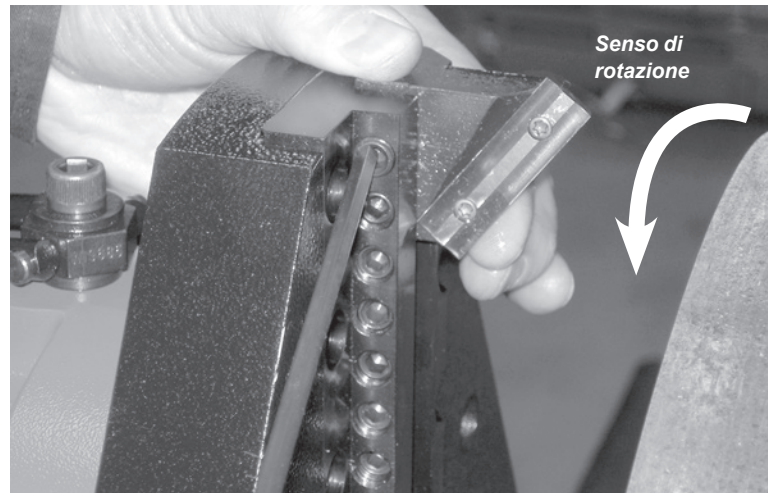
Inserire l'utensile nel portautensili e serrare le viti di fissaggio che lo trattengono. Assicurarsi che il bordo di taglio dell'utensile sia rivolto nella direzione di rotazione, come mostrato.
